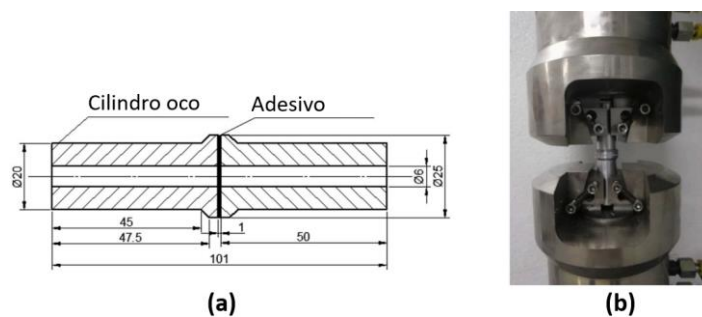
Dimensões (a) e fixação da junta topo a topo (b), adaptado de [20]
